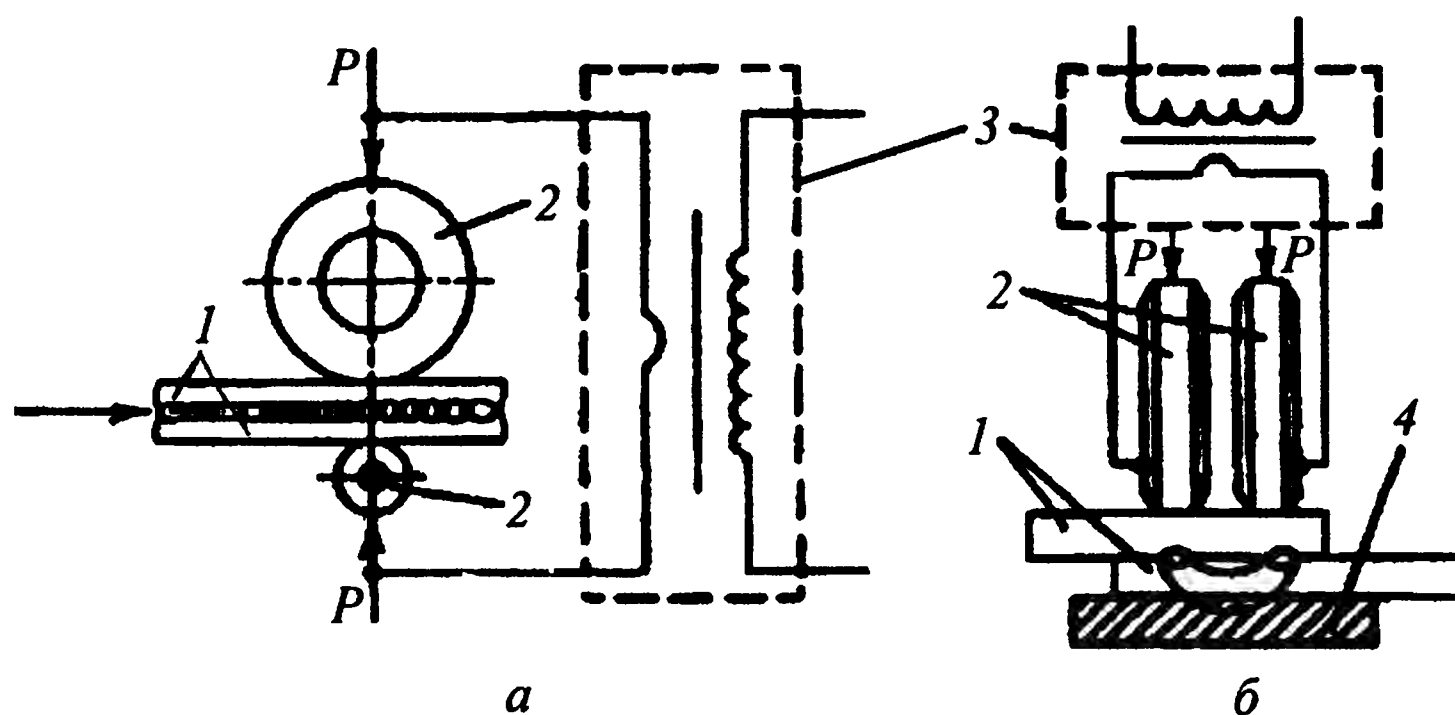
Схема шовной двусторонней (а) и односторонней (б) сварки: 1 — свариваемые детали; 2 — сварочные ролики; 3 — сварочный трансформатор; 4 — медная прокладка
